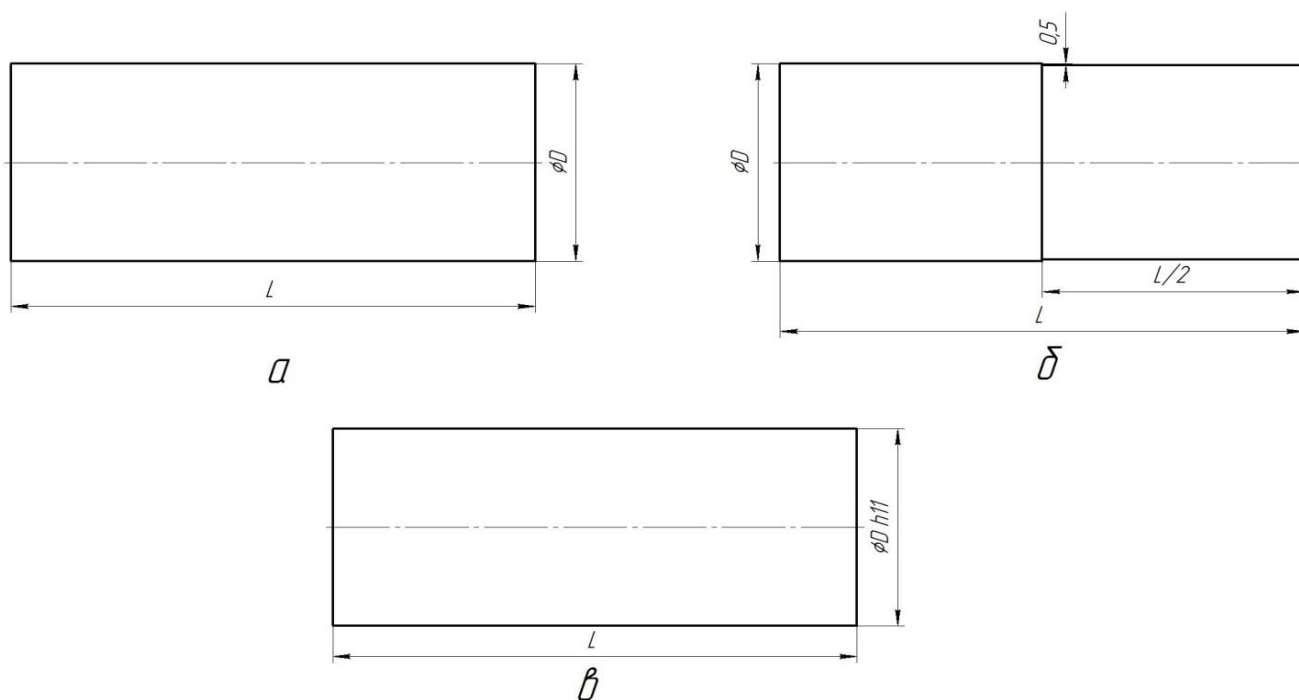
Типы используемых заготовок: а – по ГОСТ 2590-2006, б – частично обточенный из заготовки ГОСТ 2590-2006; в – по ГОСТ 14955-77 по h11 качеству.
